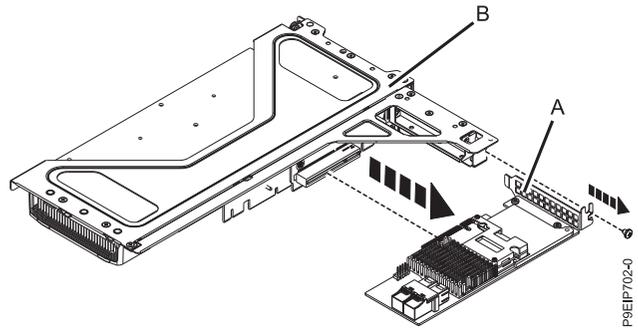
Removendo um adaptador PCIe da posição 3 do riser
